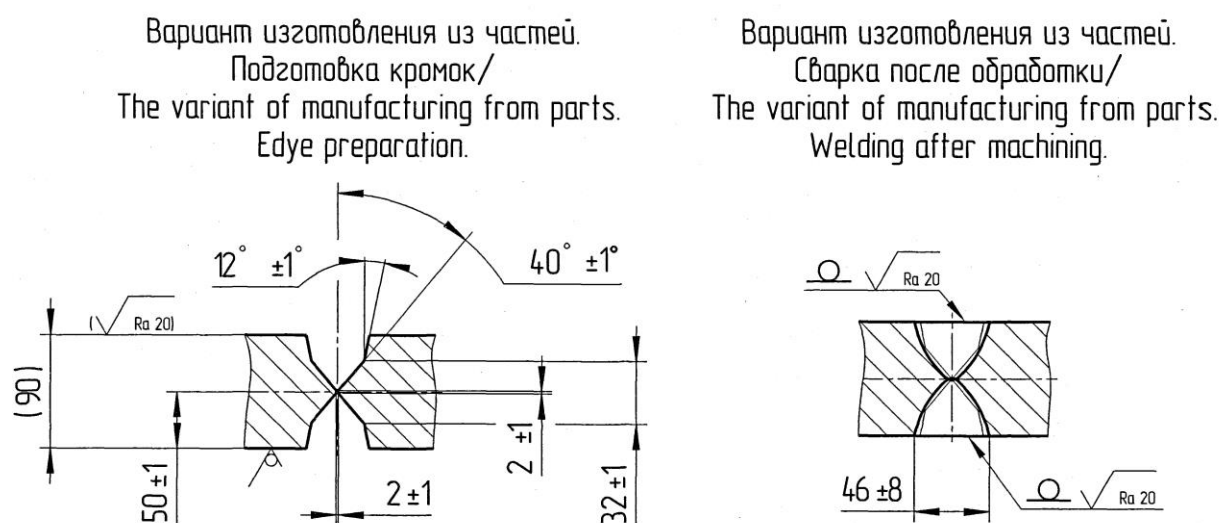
Подготовка кромок и сварной шов при выполнении опоры
